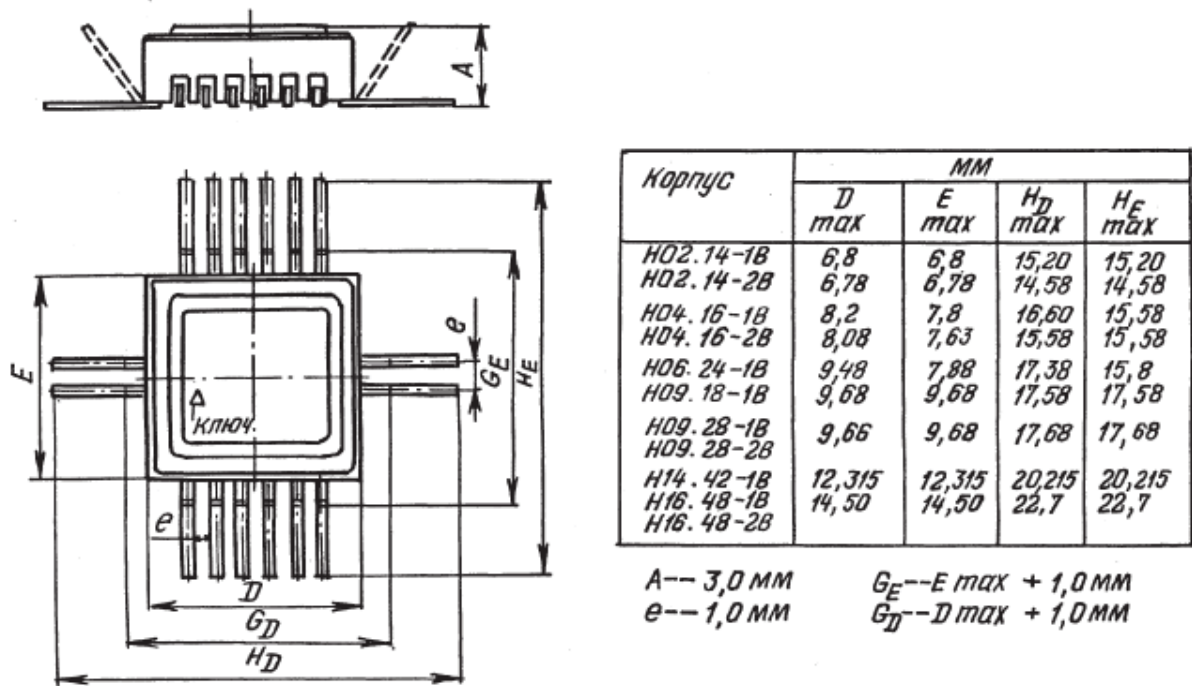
Габаритный чертеж корпуса H14.42-1B
